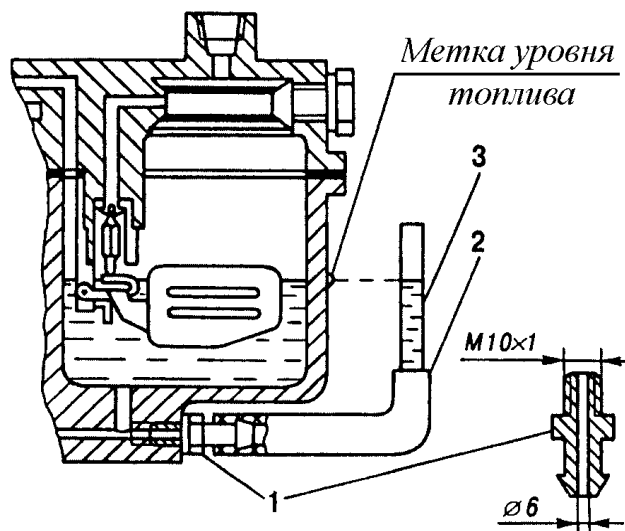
Схема проверки уровня топлива в поплавковой камере:
